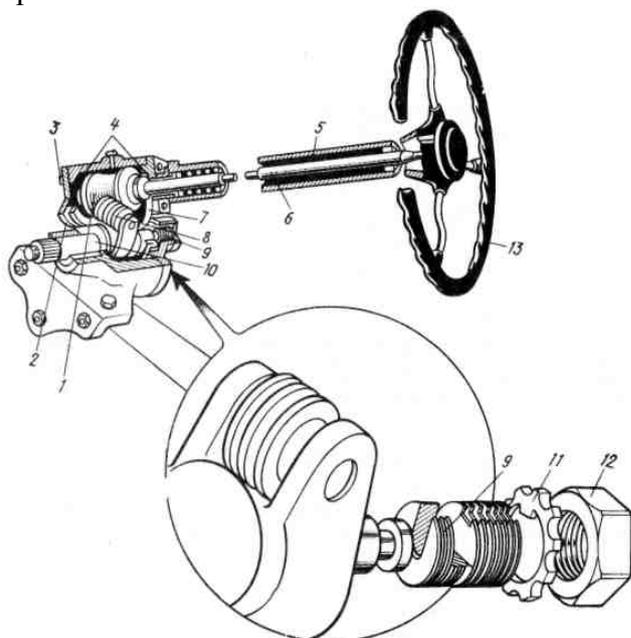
Регулировка рулевого механизма автомобиля ГАЗ – 53 А.
